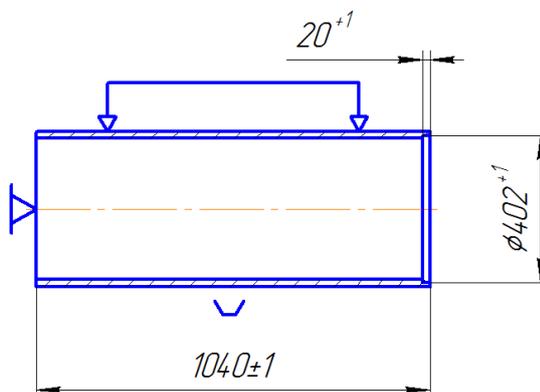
Эскиз базирования заготовки на 005 горизонтально-расточной операции.
